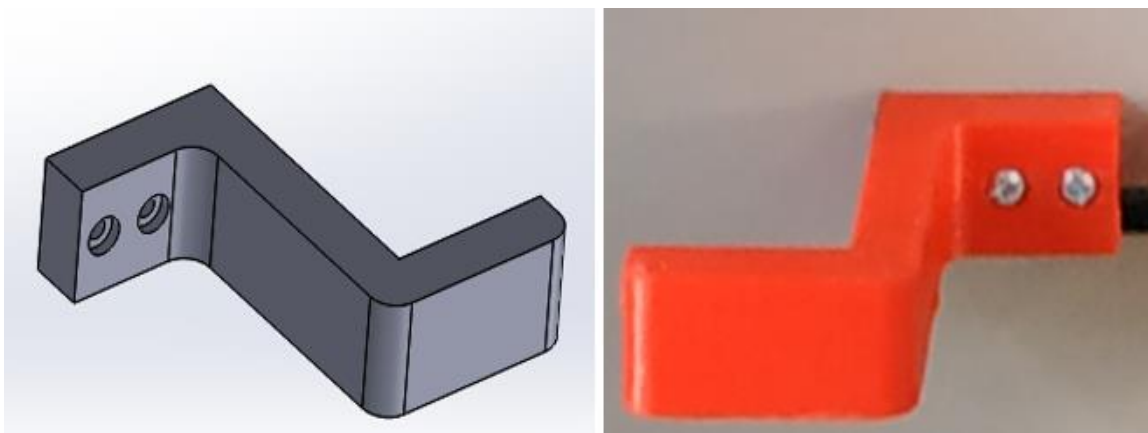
Diseño CAD /Realidad Soporte de fácil acople para fuente de 360 W.
